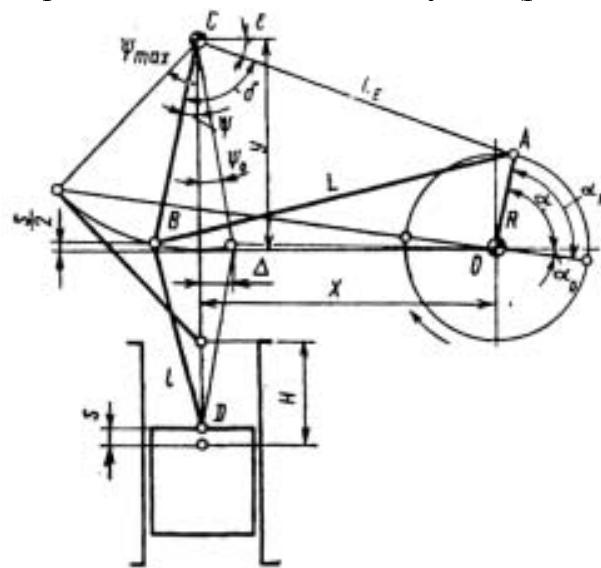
Кинематическая схема коленно-рычажного механизма пресса
